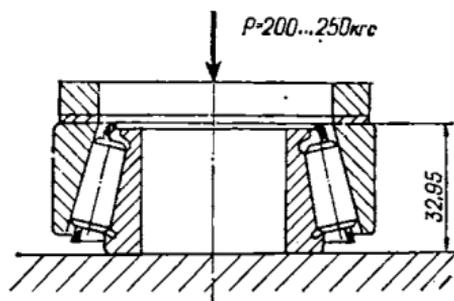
Замер монтажной высоты подшипника ведущей шестерни главной передачи
